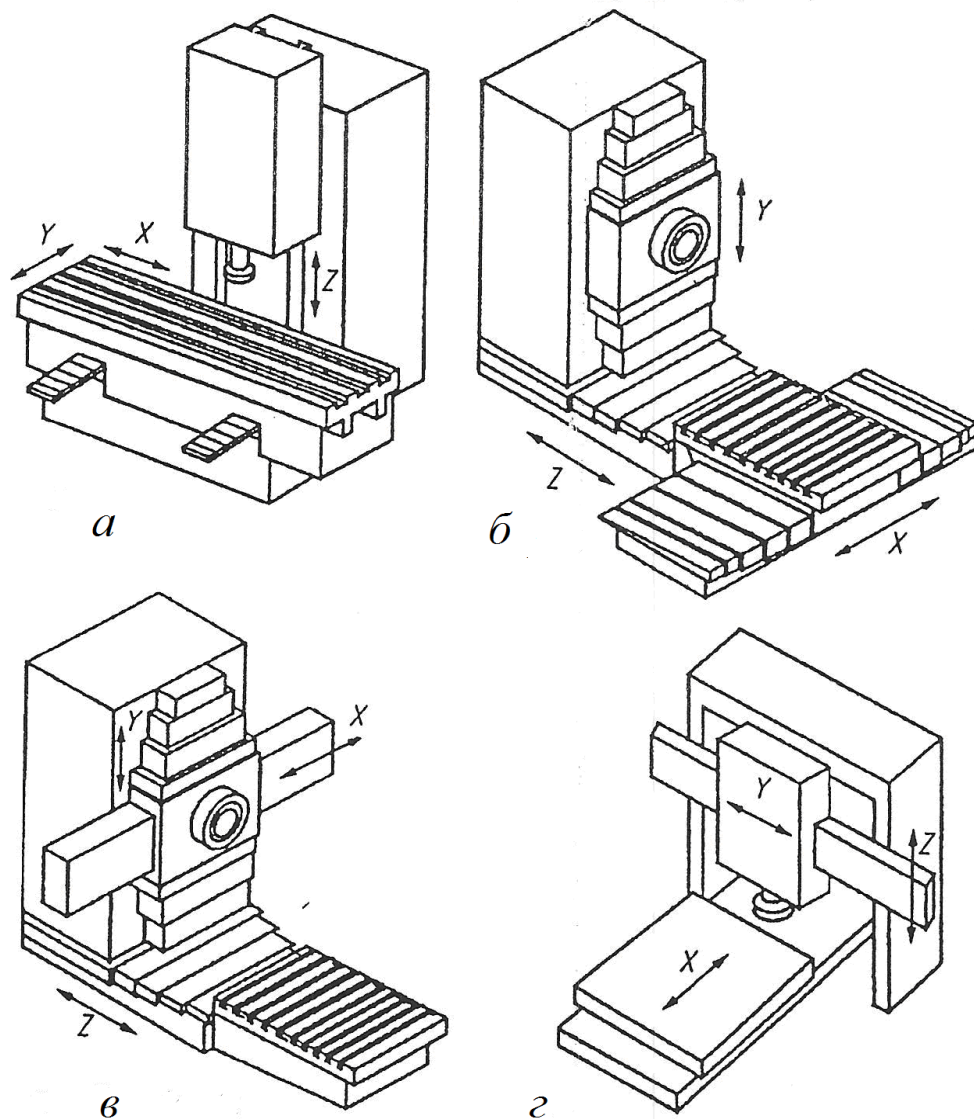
Схеми компоновки верстатів свердлильно-фрезерно-розточувальної групи
